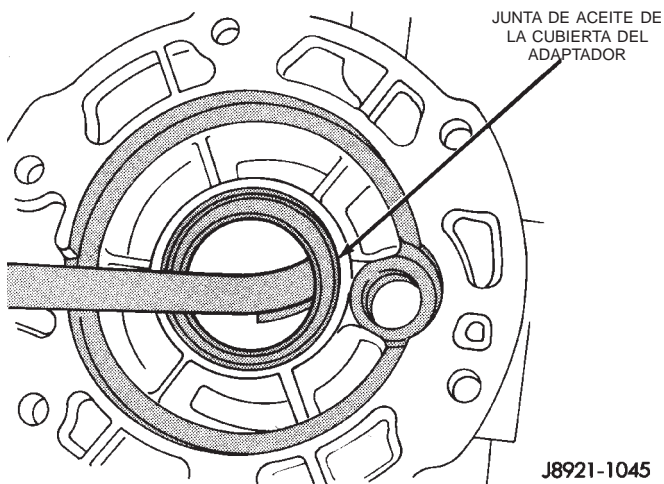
Desmontaje de la junta de la cubierta del adaptador
